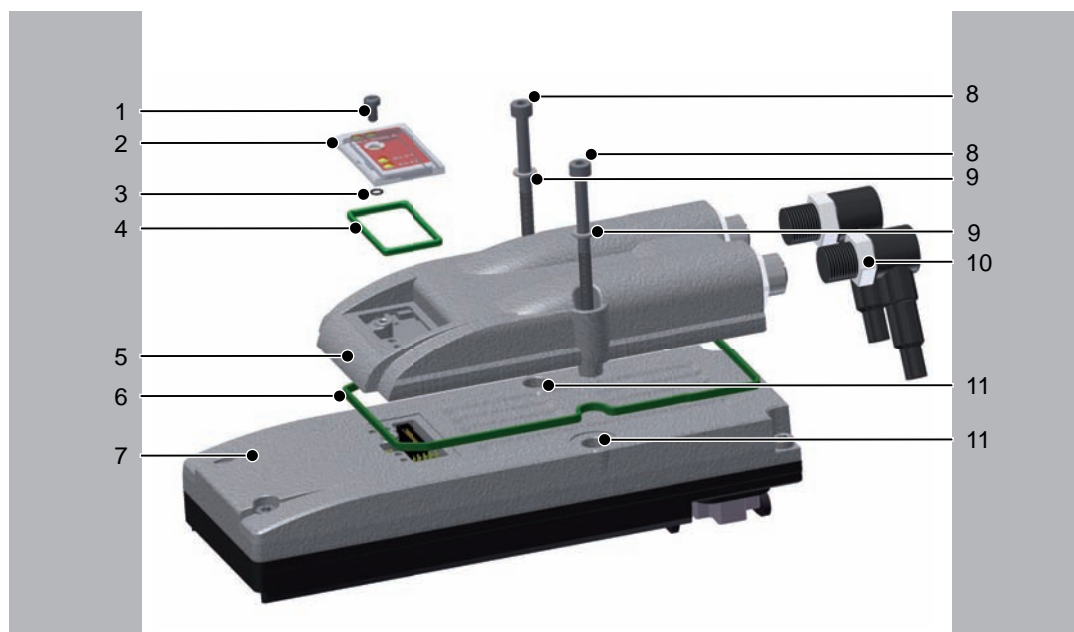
Montage des ILM62-DIO8 Optionsmoduls auf dem ILM62 Motor
